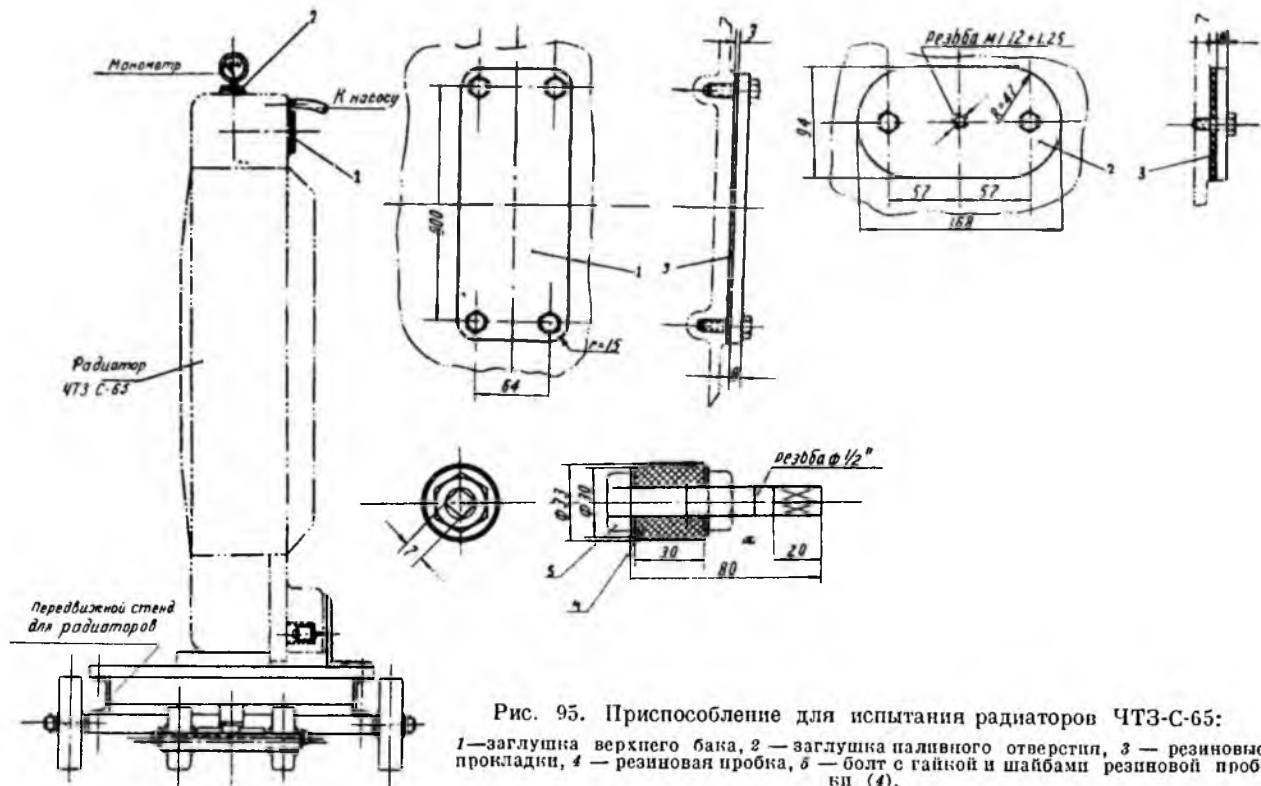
Приспособление для испытания радиаторов ЧЗС-65:
